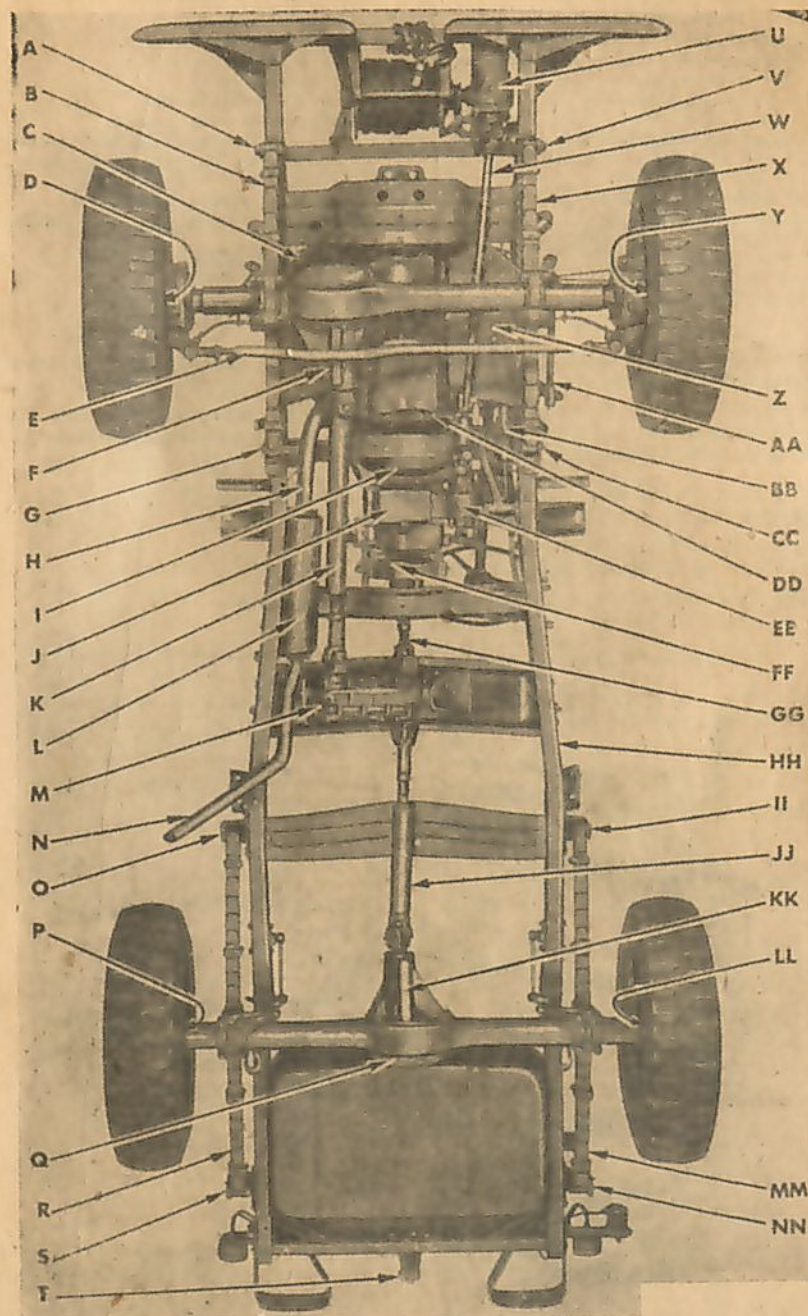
Vue par dessous du châssis 3/4 T. 4 × 4 :
